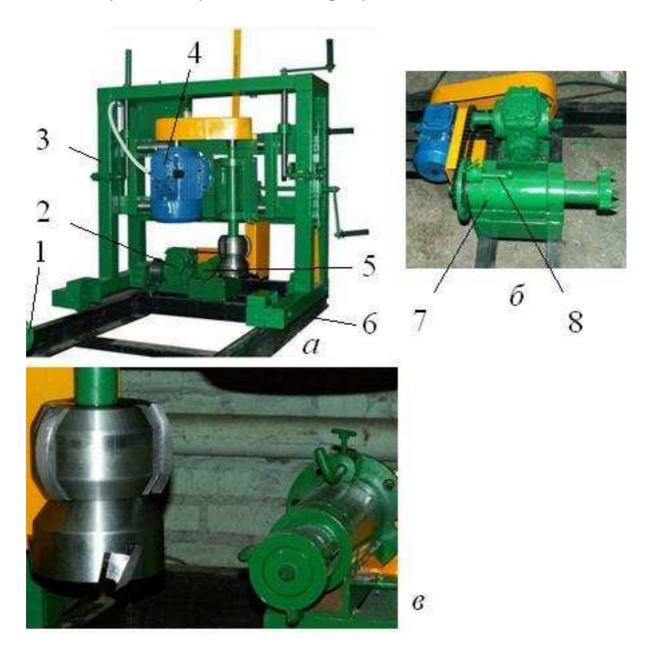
Станок оцилиндровочный модели Тайга ОС-1:
